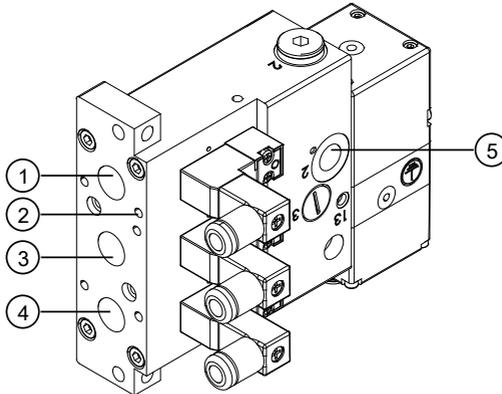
Gasanschluss 2- und 3-Gas-Variante mit oder ohne Filter
